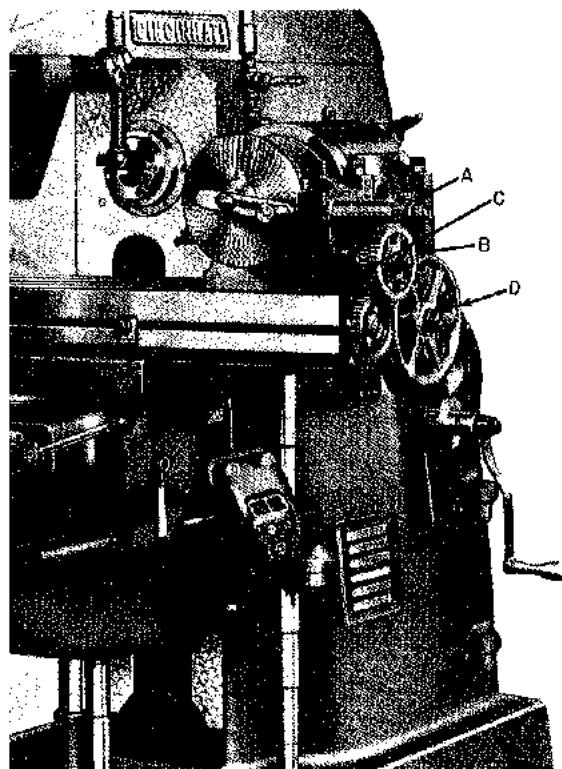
Fresadora con los engranajes dispuestos para el fresado helicoidal (Cincinnati Milling Machine Co.).
